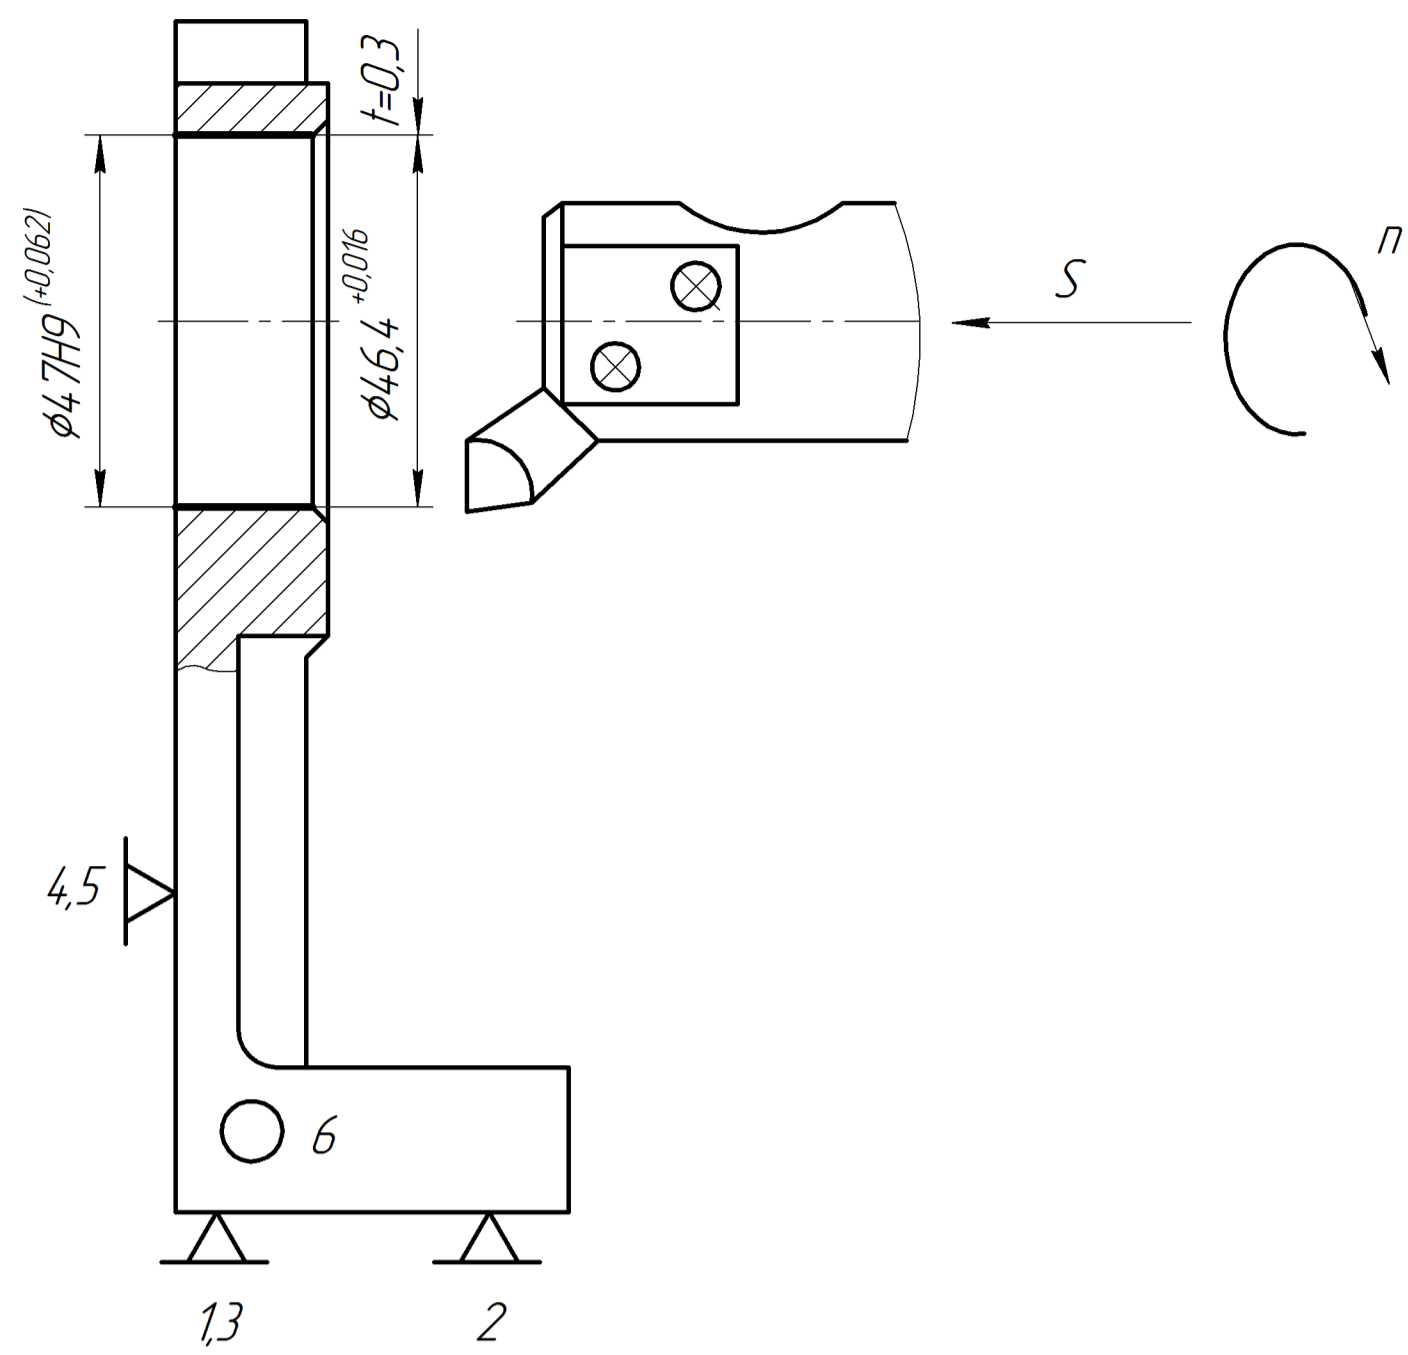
Ескіз обробки: Верстат свердильно-фрезерно-розточний мод. 6904ВМФ2; різець розточний 2142-0013 ГОСТ 9795-84 оснащений пластиною із твердого сплаву Т60К6, розміри державки 8×8 мм; геометрія різальної частини: $\varphi=90^\circ$; $\varphi_1=90^\circ$; $r=1,0 \text{ мм}$; $\gamma=0^\circ$; $\alpha=8^\circ$; $\lambda=0^\circ$; режими різання: $V=184,5 \frac{\text{м}}{\text{хв}}$; $S=0,16 \frac{\text{мм}}{\text{об}}$; $n=1250 \text{ хв.}^{-1}$; $t=0,3 \text{ мм}$.
